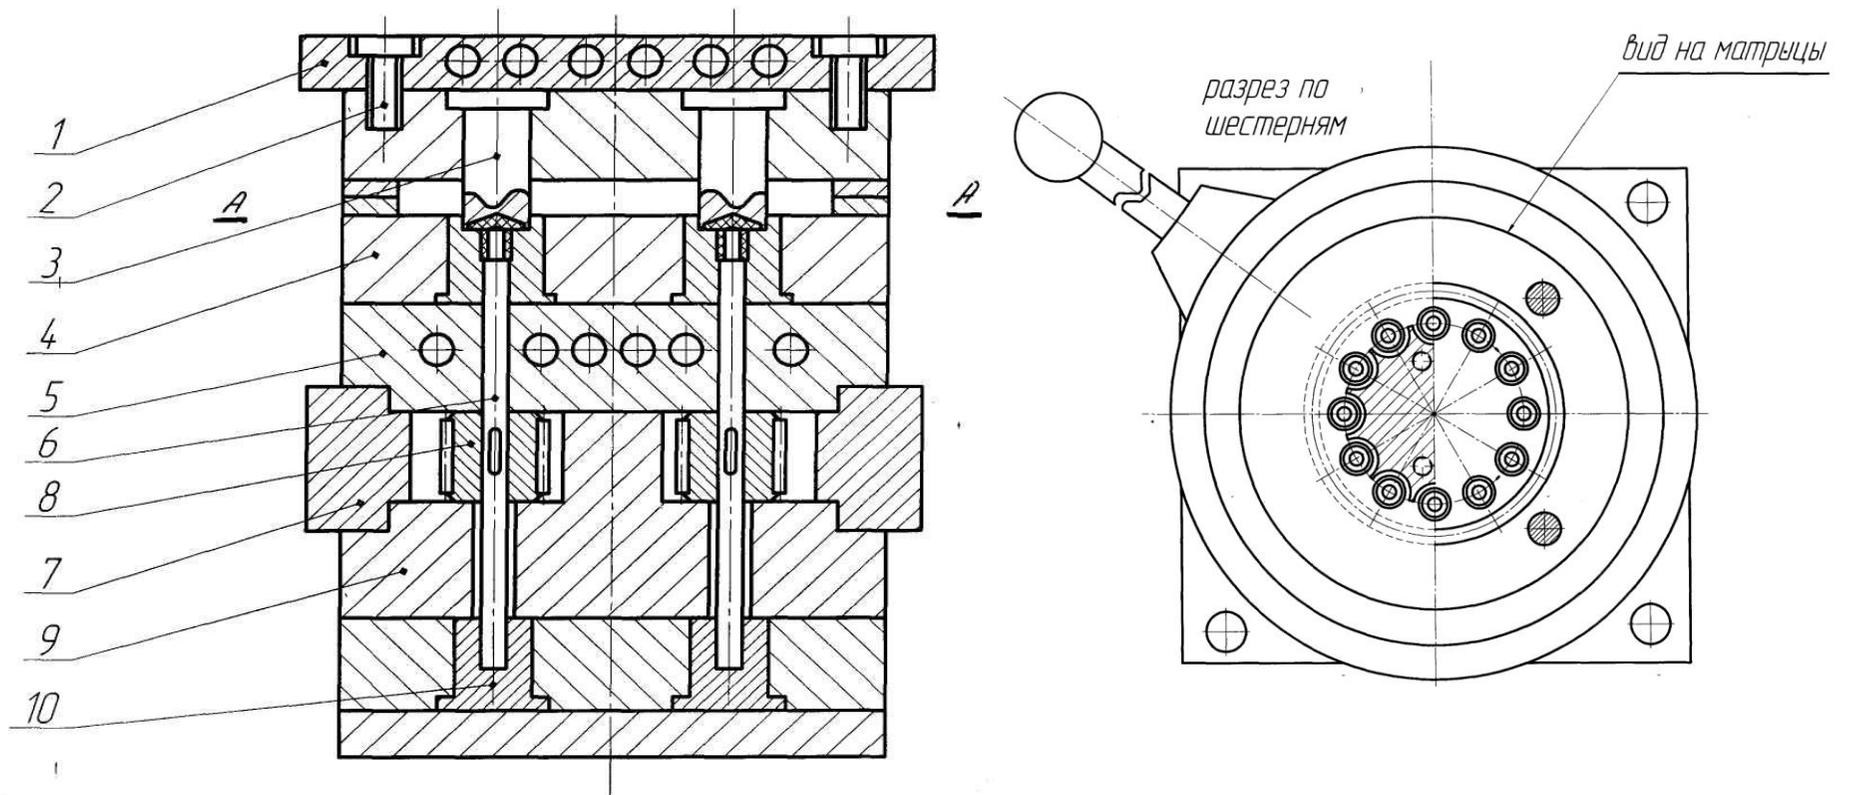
Пресс-форма для изготовления изделий методом прессования:
